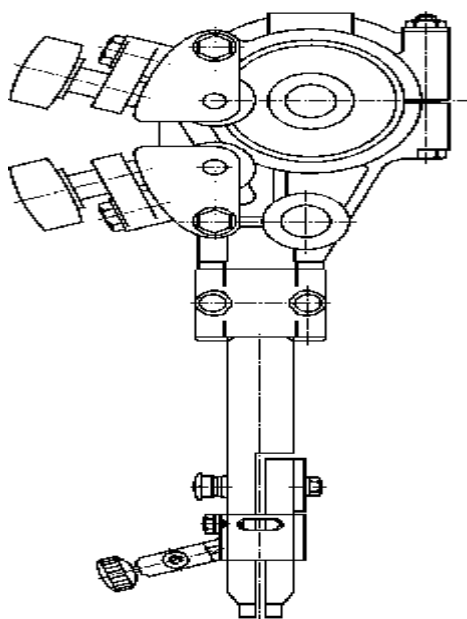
Головка для сварки под слоем флюса
